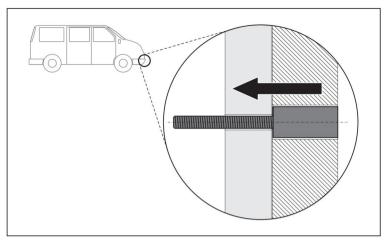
Sentido de montagem dos parafusos espaçadores 1 travessa metálica, 2 rodapés
